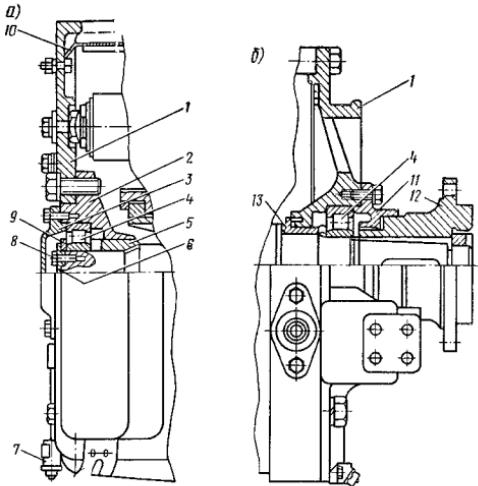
Передний (а) и задний (б) подшипниковые щиты
